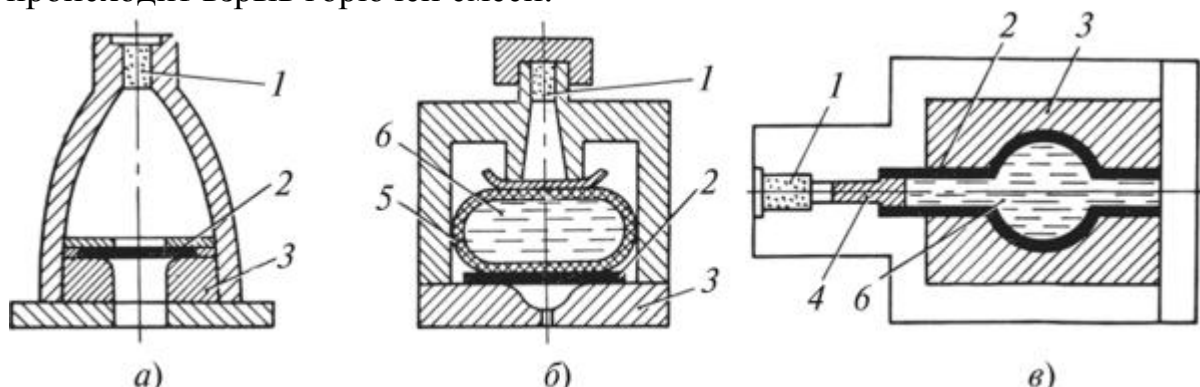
Схемы установки для штамповки взрывом пороха
